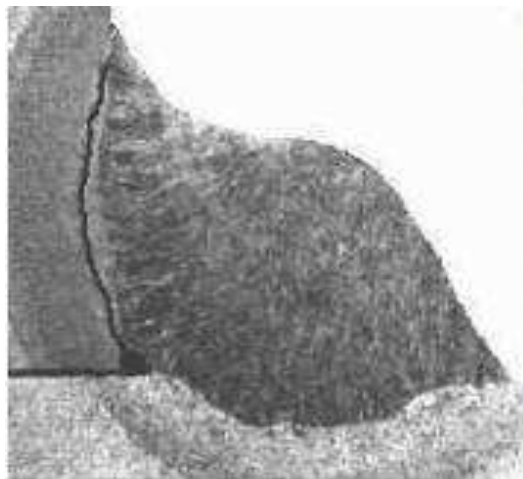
Junta soldada realizada con método erróneo de soldadura.
